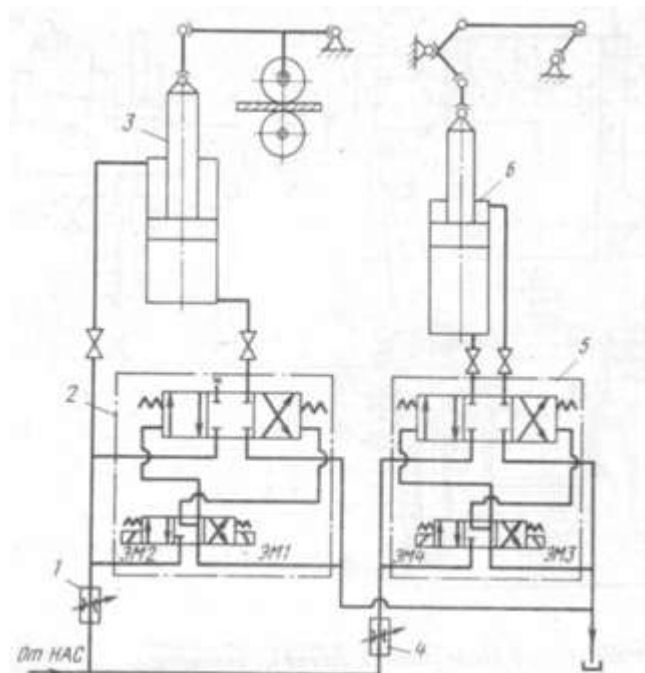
схема гидравлическая верхнего ролика тянущеправильной машины и поворотного лотка машин непрерывного литья заготовок
